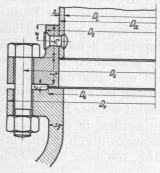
Flanschverbindung mit angenietetem Rohr.
